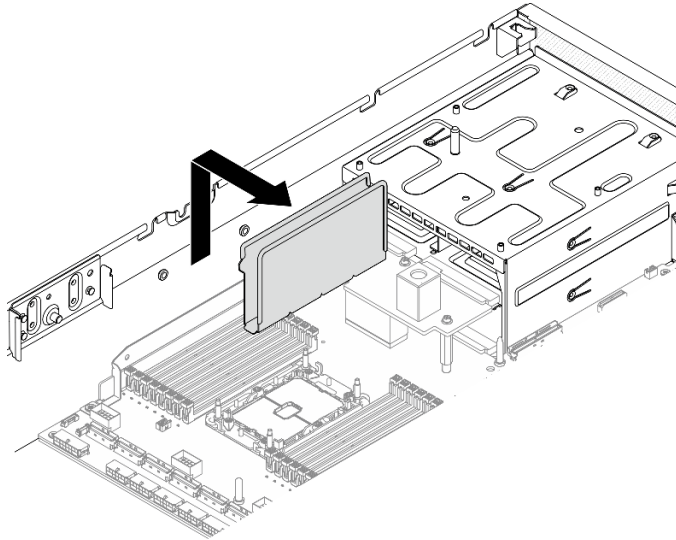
Entfernen der Kabelführung aus dem Gehäuse
